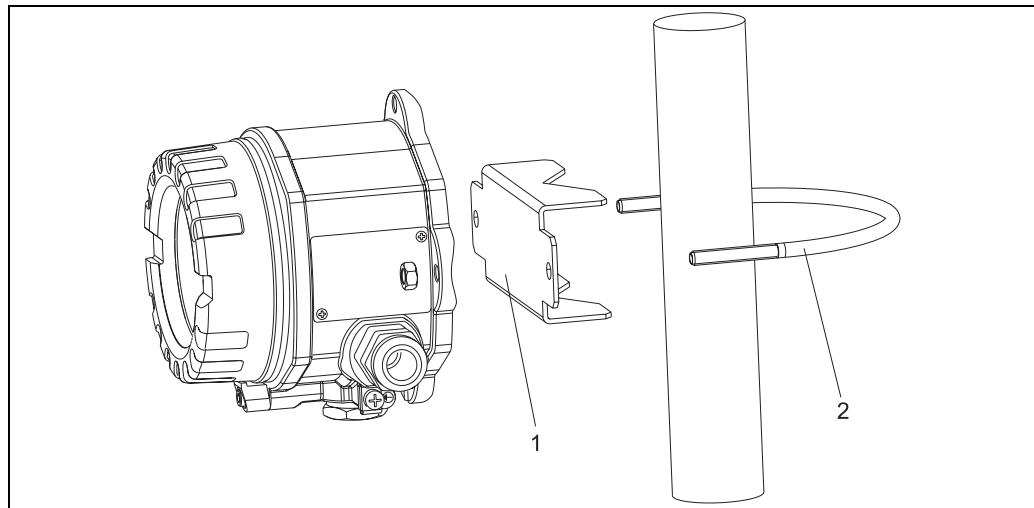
Rohrmontage des RIA141 mit Montagehalter für Rohrdurchmesser 1,5-2,2"
